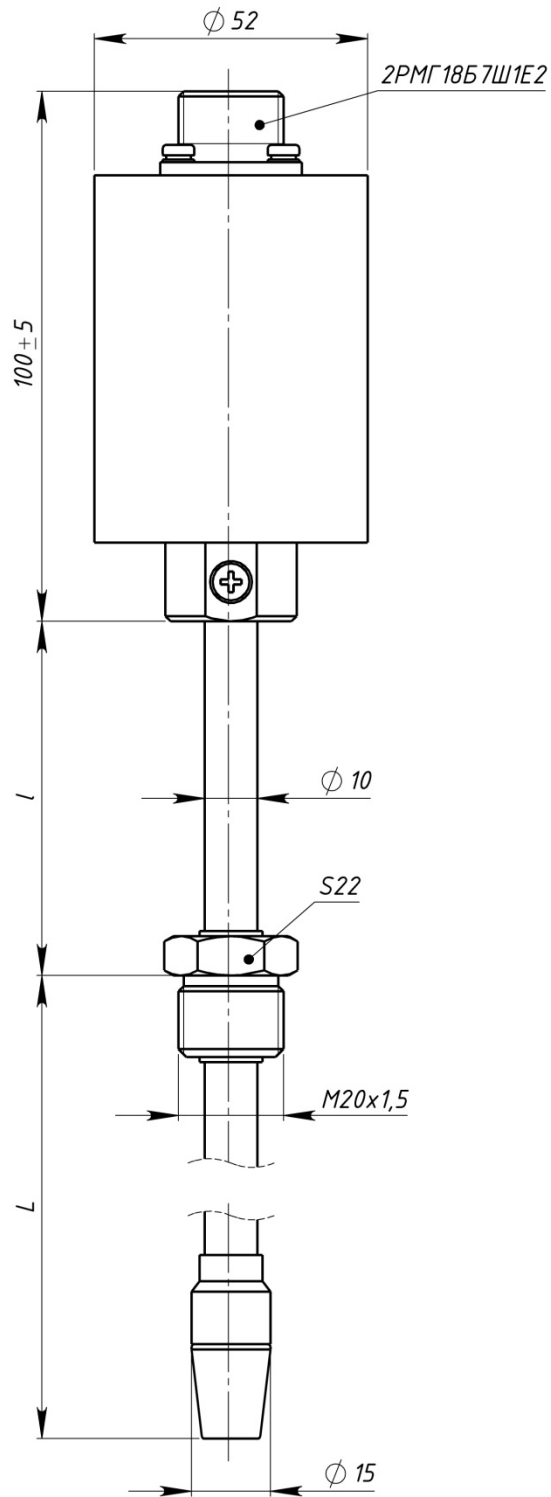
Габаритно-монтажные размеры исполнения ПТВ-1/М1-1 (в корпусе типа НГ-1)
